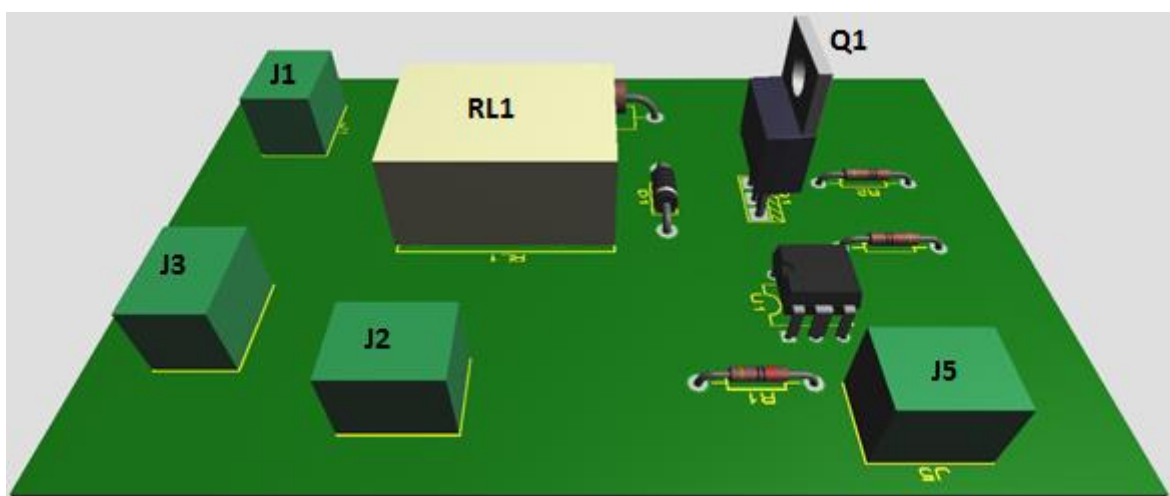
Diseño del PCB en 3D del circuito para el control de las válvulas.
